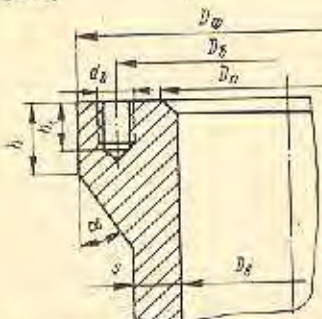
Основные размеры цельноконического фланца (при сварного или заодно с корпусом аппарата) для $p_y > 10 \text{ Мн/м}^2$.
